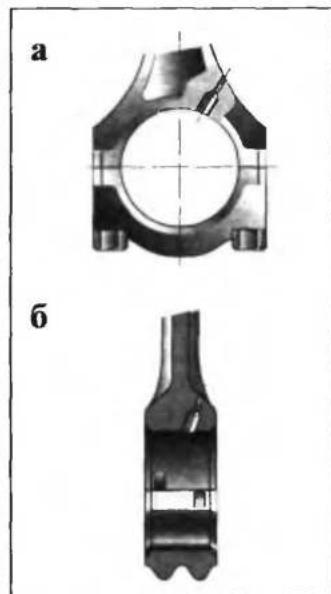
Варианты подачи масла для смазки цилиндров через шатун: а — традиционная конструкция; б — конструкция FIAT
